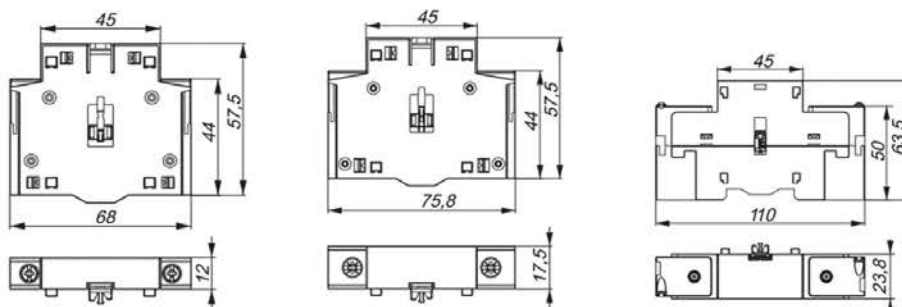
Габаритные и установочные размеры контактов дополнительных / Figure 5 – Overall and mounting dimensions of auxiliary contacts
